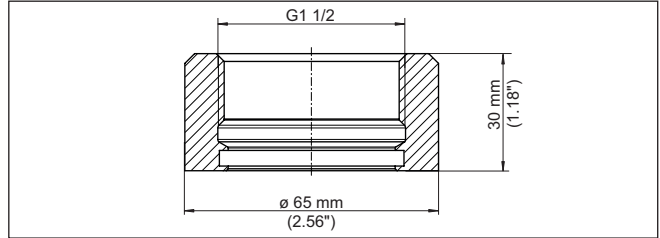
Maße Einschweißstutzen Gewinde G1½ (ISO 228-1) - Hygienedesign
